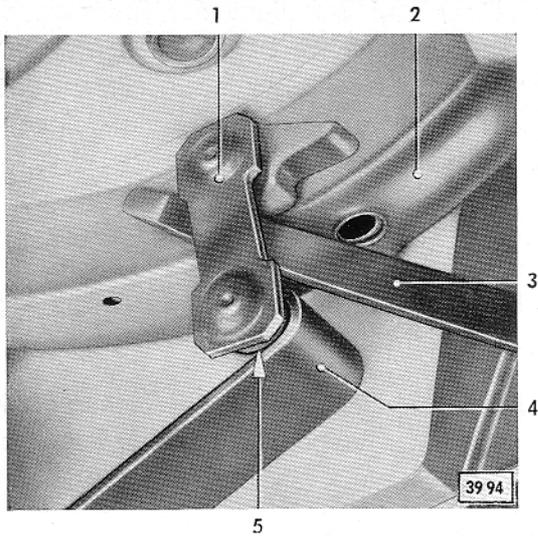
An der rechten hinteren Federaufhängung Lasche mit Gehängebolzen aus Aufnahme im Unterbaulängsträger und aus Federauge herauszwingen
